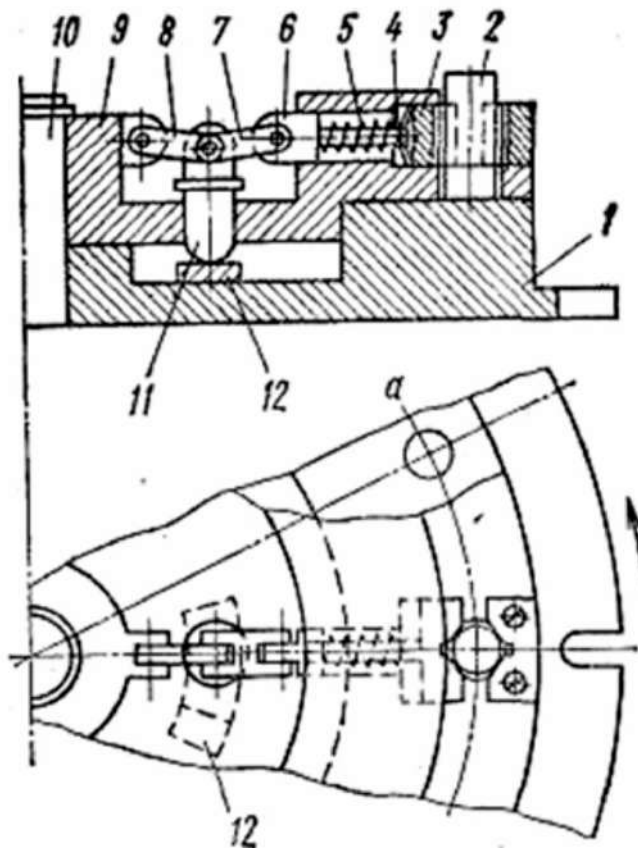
Схема затиску заготовок на столі карусельно-фрезерного верстата з приводом від обертання столу
